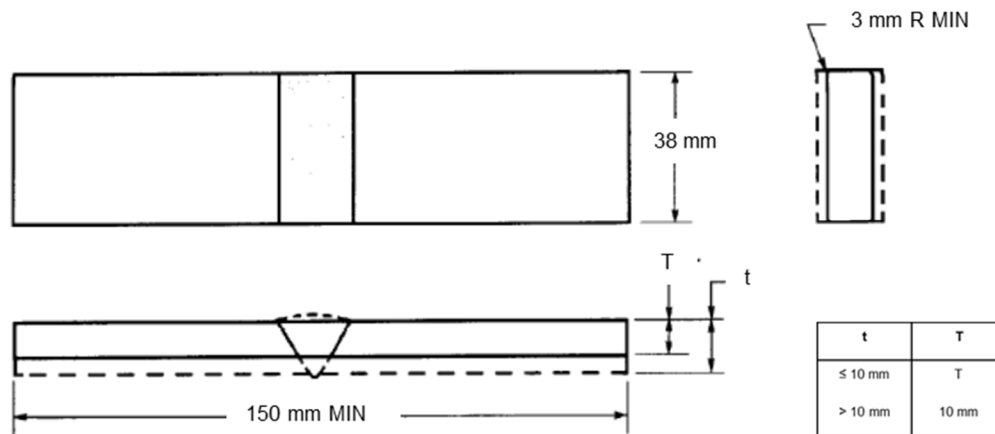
Esquema probeta prueba de doblez. Figura A.7. (AWS, Standard Methods for Mechanical Testing of Welds, 2010)
